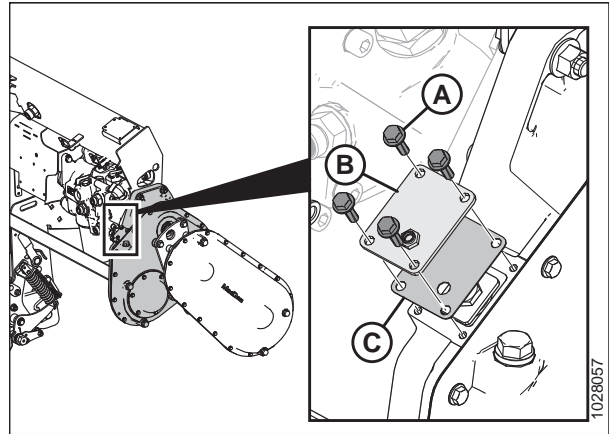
Крышка натяжителя цепи главного редуктора
